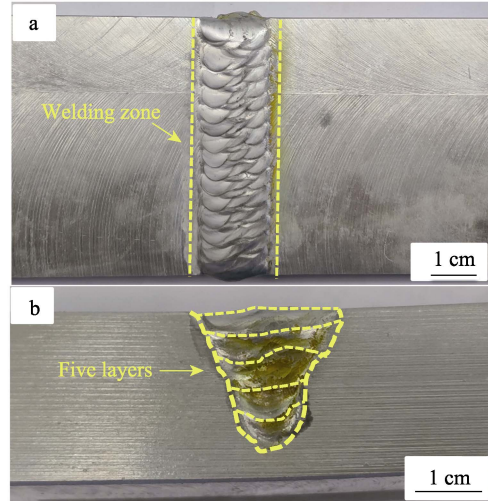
焊接接头的表面形貌 (a) 和横截面形貌 (b)
